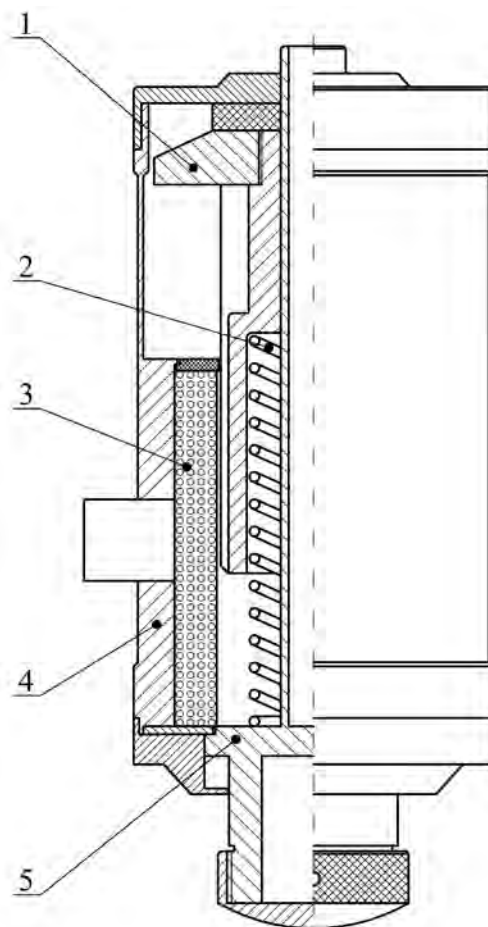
Сводообрушитель с ЛЭМД: 1 – якорь; 2 – пружина; 3 – обмотка; 4 – корпус-статор; 5 – наковальня.
